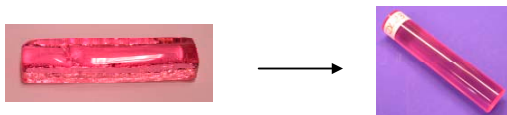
Vom Glasblock zur Preform durch mechanische Bearbeitung.
